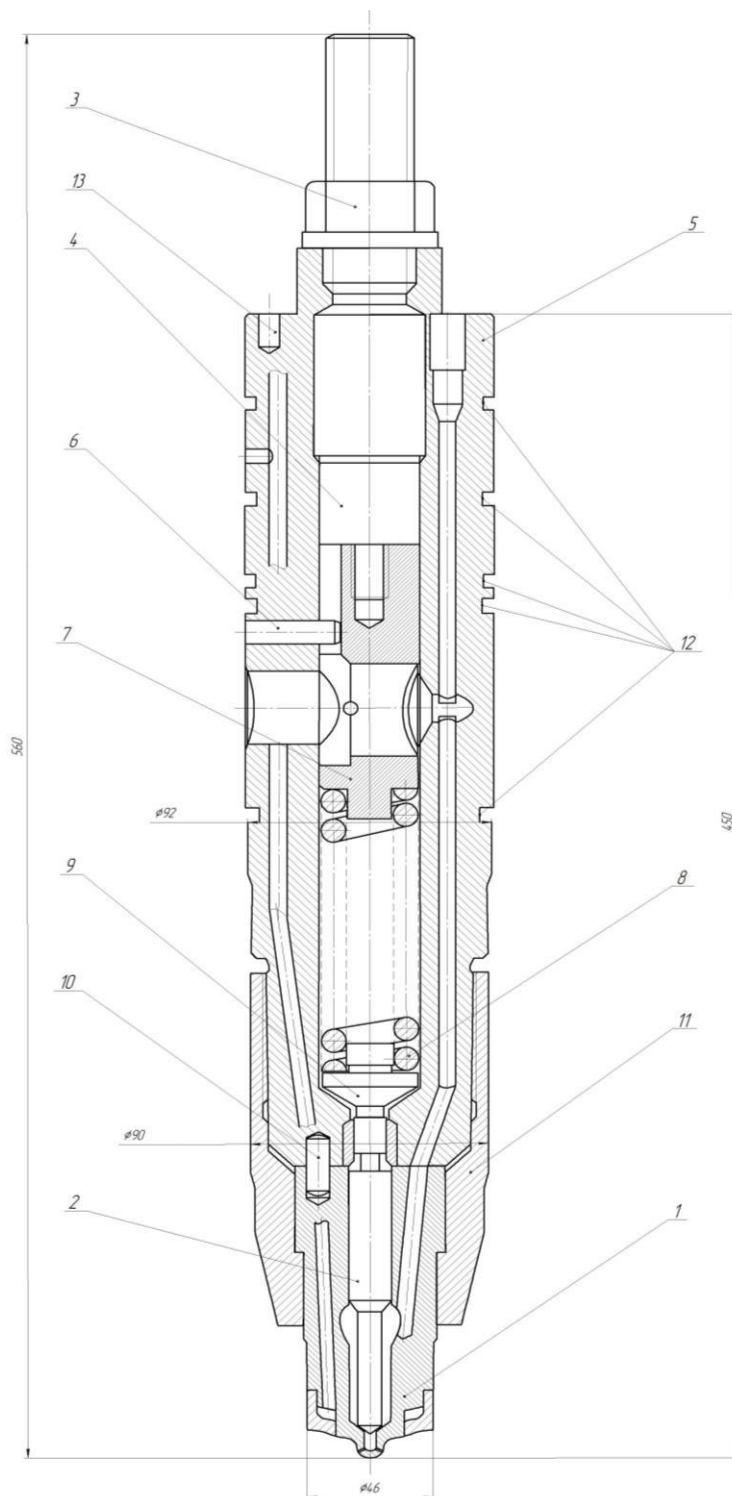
Форсунка суднового дизеля 8L 58/64: 1 - корпус розпилювача; 2 – голчастий клапан; 3 – гайка шестигранна; 4 – упор навантажуючої пружини; 5 – корпус форсунки; 6 – упор фіксуючий; 7 – нижня опора навантажуючої пружини; 8 – навантажуюча пружина стиснення; 9 – штанга приводу голчастого клапану; 10 – штифт; 11 - гайка насадки; 12 – проточування під О-подібні кільця ущільнення; 13 – отвір під фіксатор
